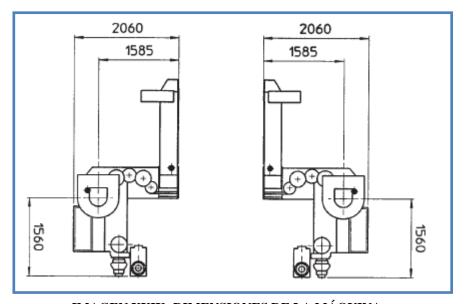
IMAGEN XXIX: DIMENSIONES DE LA MÁQUINA
